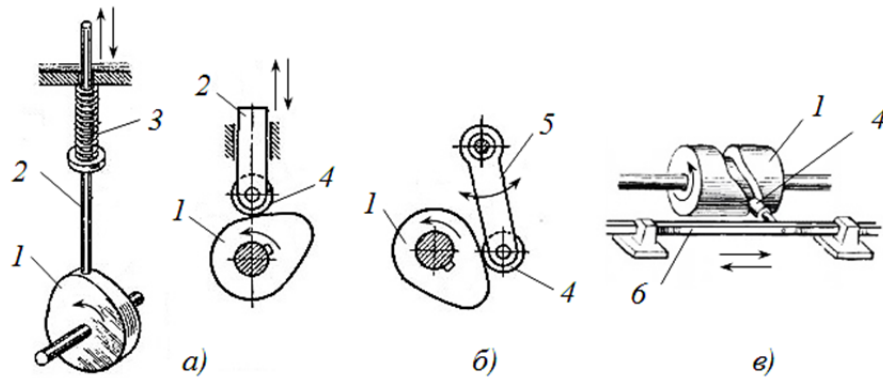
Схеми кулачкових механізмів: зворотно-поступального руху(а), коливального руху(б), просторовий(в) (1 – кулачки; 2 – штовхачі; 3 – пружина; 4 – ролики; 5 – коромисло; 6 – планка).
